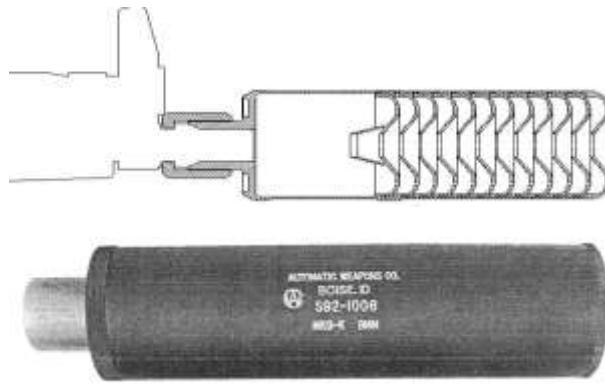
Конструктивная схема глушителя R16MP5 и внешний вид глушителя MK-9K
